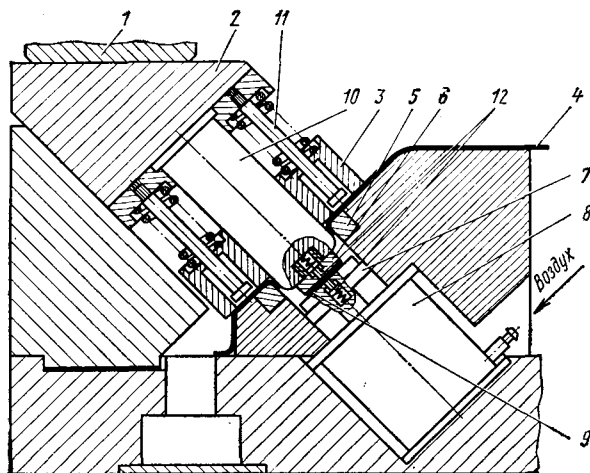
Штамп для совмещенной пробивки и отбортовки отверстия в горловине корпуса бензобака
